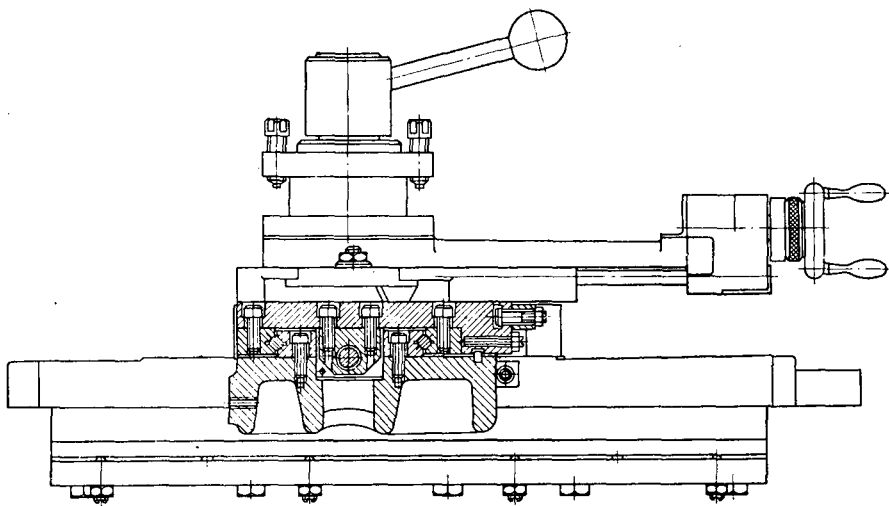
Направляющие качения для поперечных салазок станка 97ИТ
